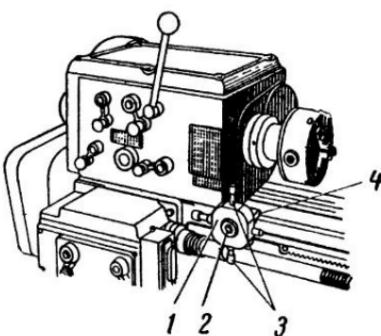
Четырехпозиционный упор для суппорта, установленный на станине токарного станка.
